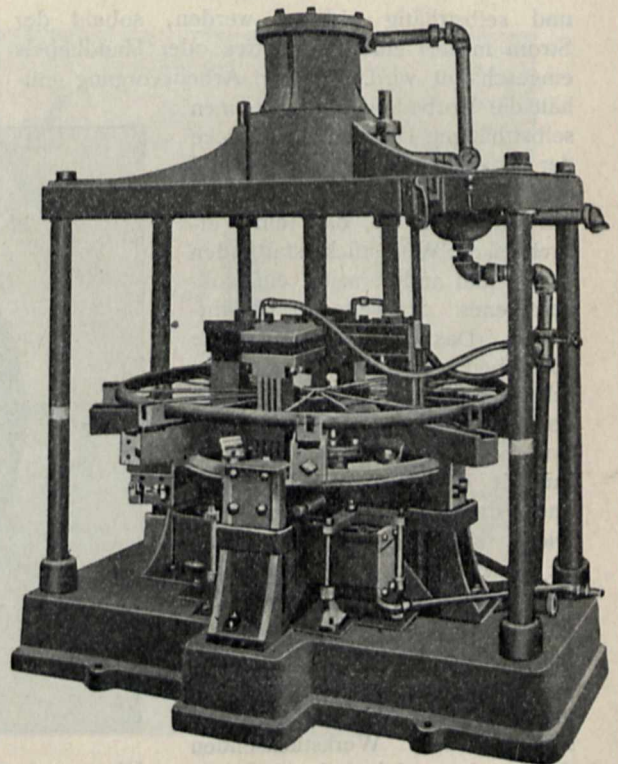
Schweissapparat Type 80A, zum Schweissen der Speichen und Naben in metallenen Rädern.
